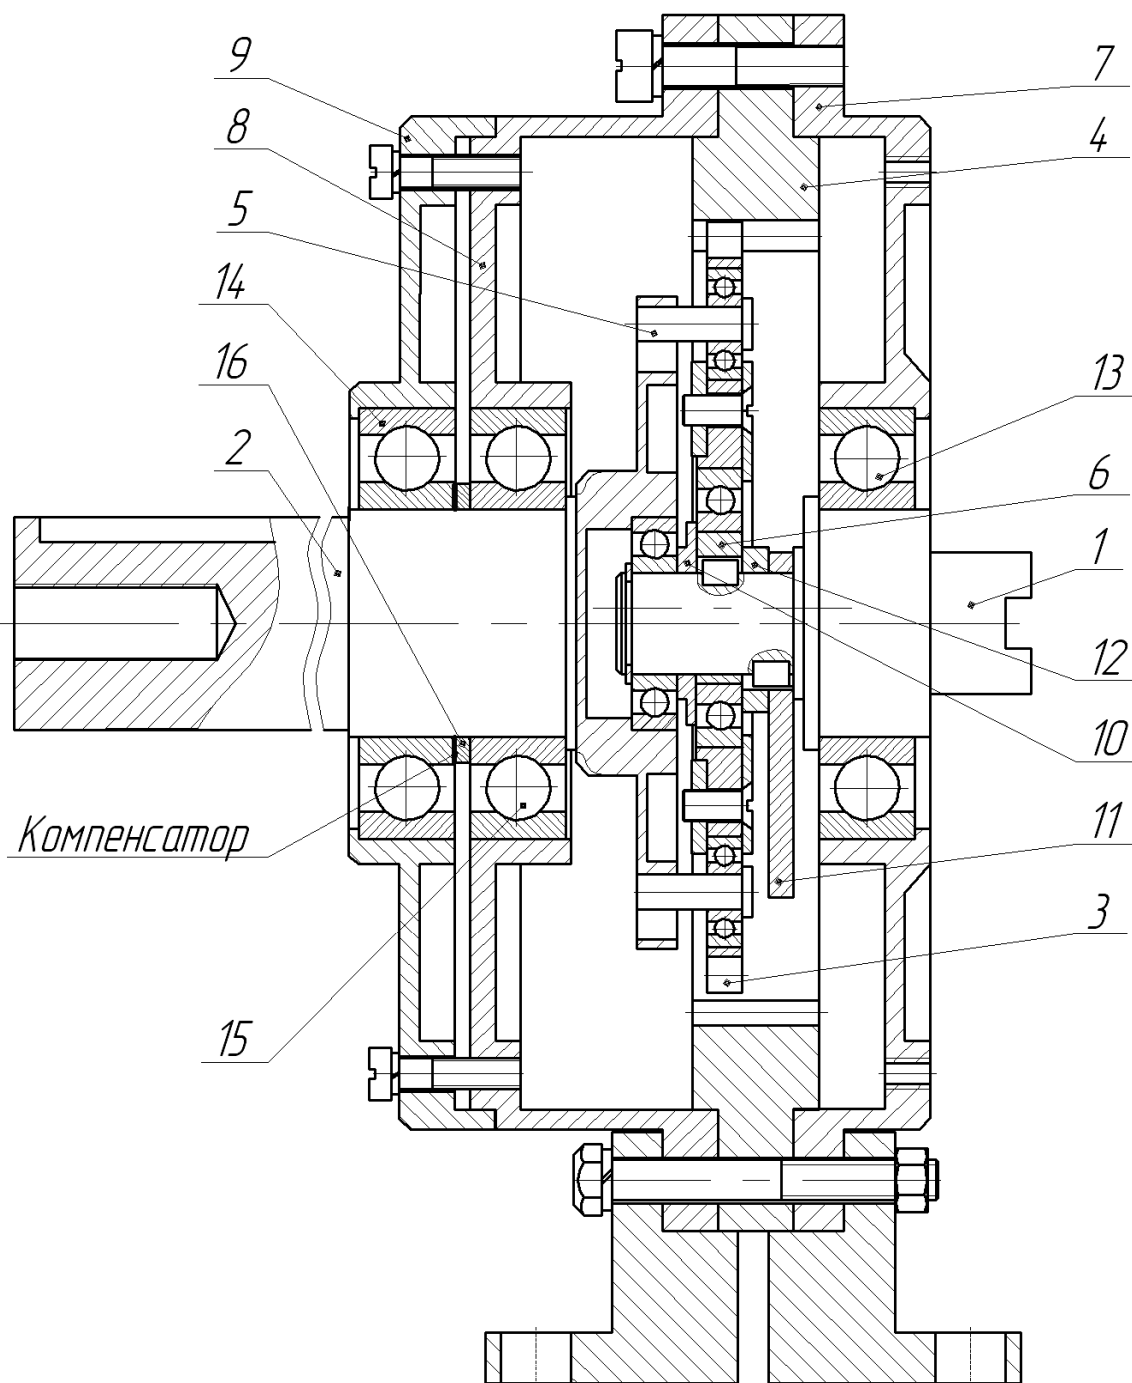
Планетарный эксцентриковый редуктор: 1 – вал ведущий; 2 – вал ведомый; 3 – сателлит; 4 – центральное колесо; 5 – палец; 6 – эксцентрик; 7...9 – крышки; 10 – кольцо; 11 – диск; 12 – кольцо; 13...15 – подшипники; 16 – распорное кольцо
